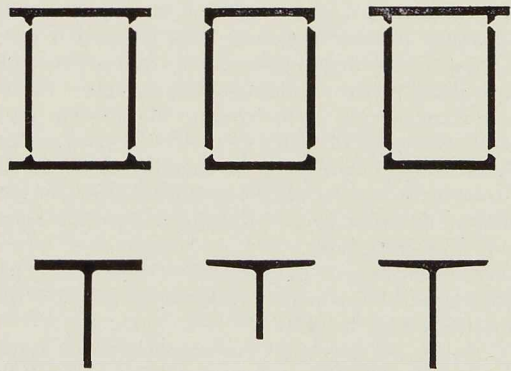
et 4. Profils spéciaux employés en soudure.
